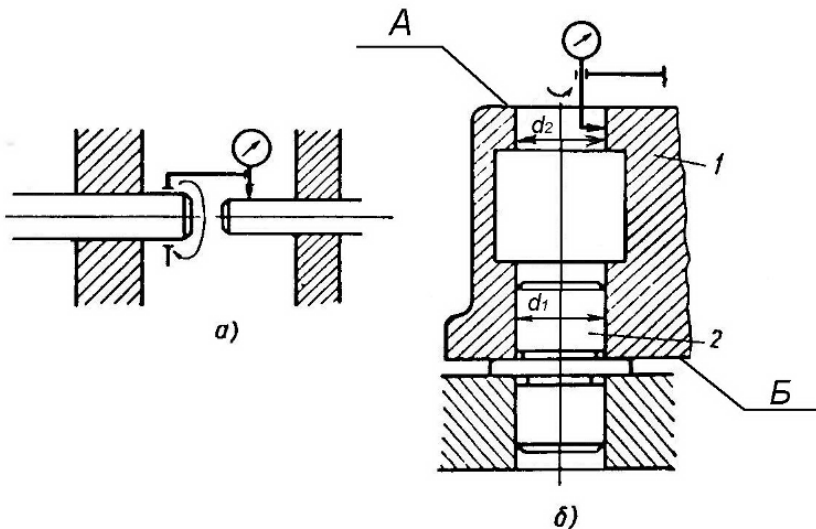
Схемы контроля соосности отверстий корпусных деталей
